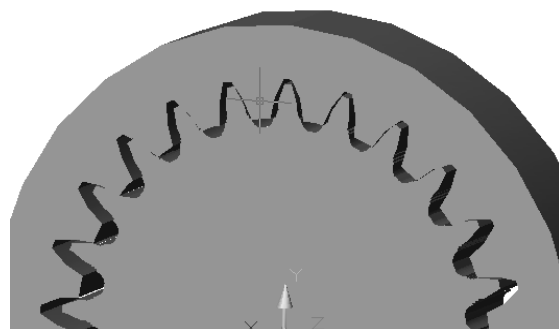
Внутреннее зубчатое зацепление с модифицированным профилем зубьев сателлита
